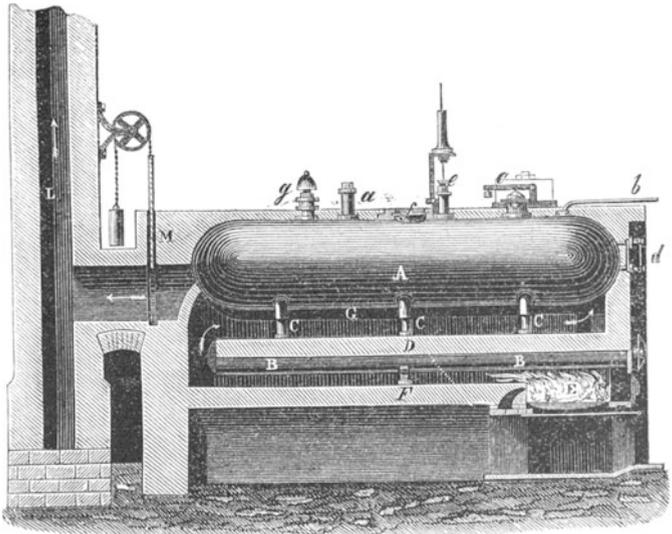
Dampfkesselanlage für Hochdruckmaschinen.
